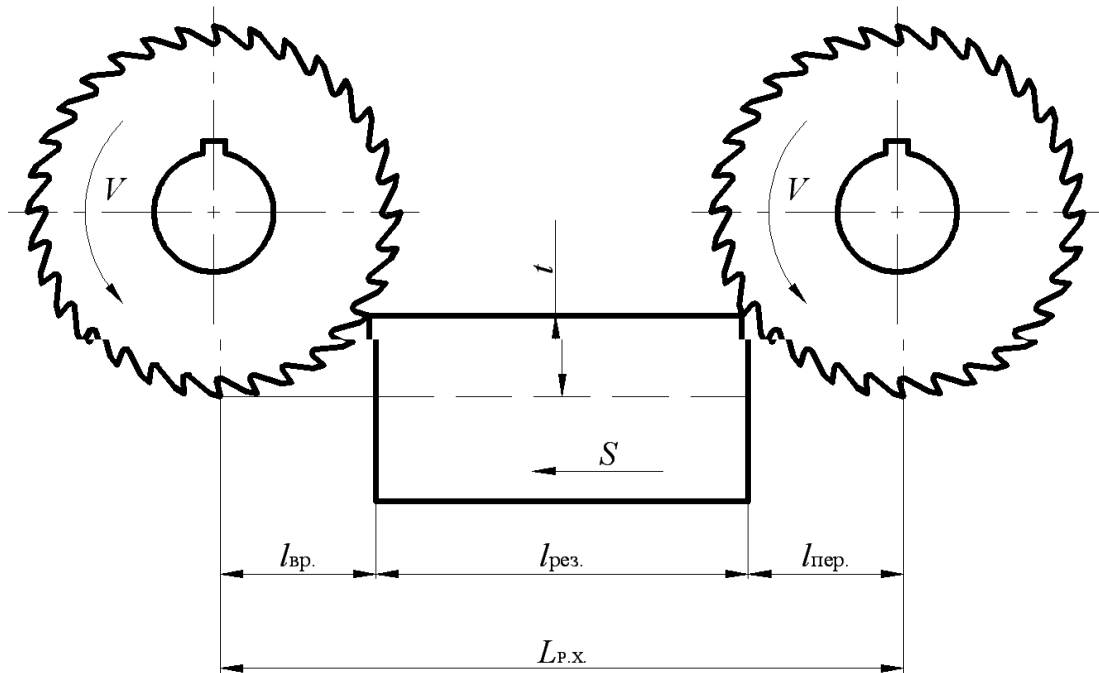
Довжина робочого ходу інструменту при фрезеруванні
